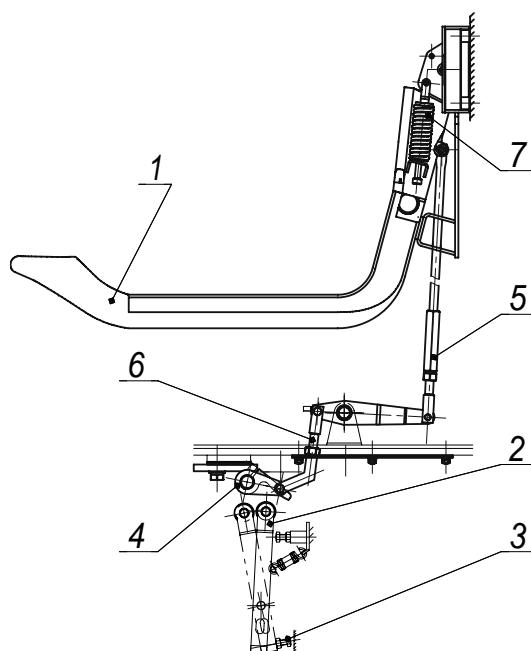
Привод управления аварийно-стояночным тормозом
